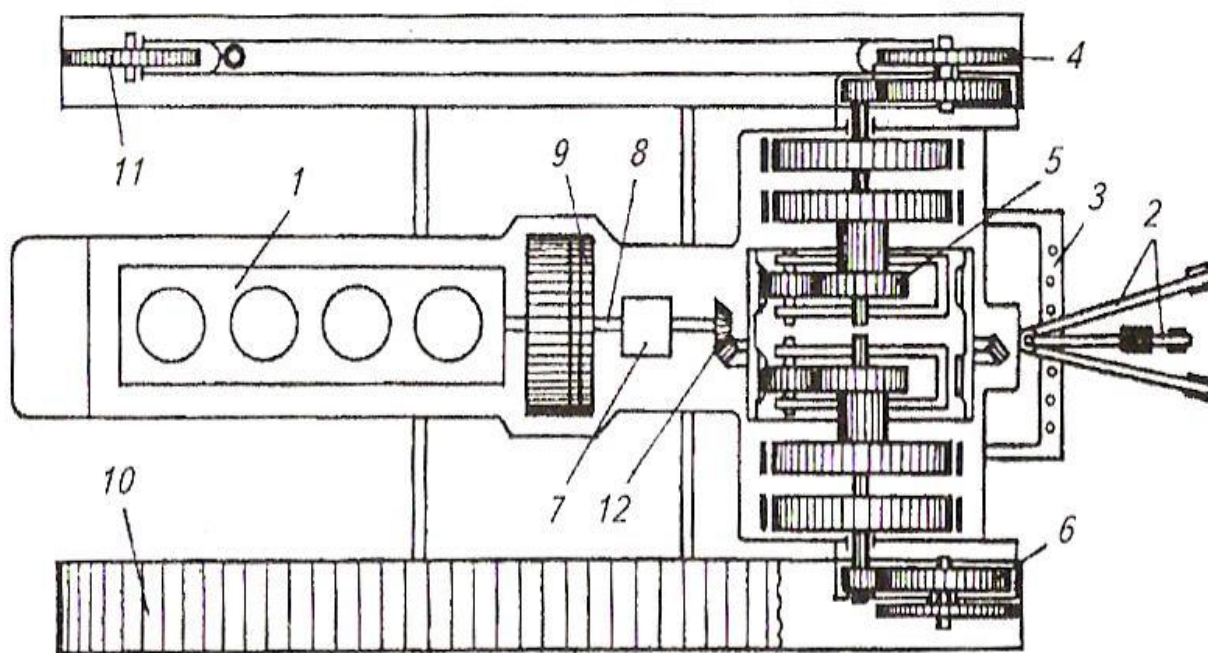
Схема расположения основных частей, механизмов и деталей гусеничного трактора:
